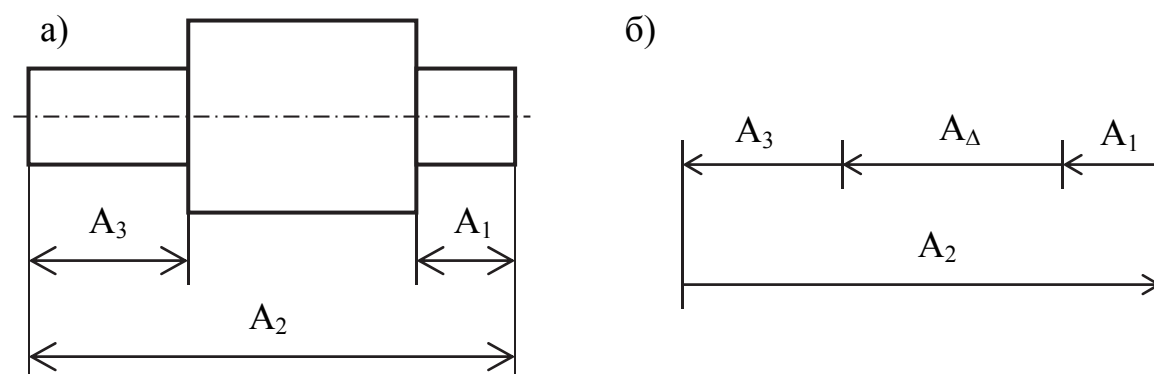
Эскиз детали (а) и схема детальной размерной цепи (б)
